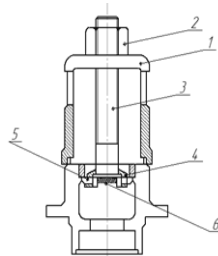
Съемник для выпрессовки обойм с помощью кулачков на пружинах
